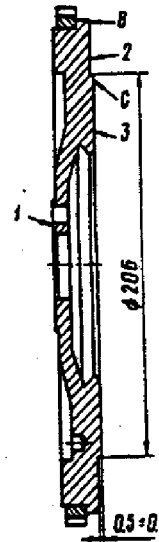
Volante: 1 - superfície de contato com o flange da árvore de manivelas; 2 - superfície de fixação do platô da embreagem; 3 - superfície de trabalho do disco; B - ponto de verificação da oscilação da superfície 2; C - ponto de verificação da oscilação da superfície 3.
